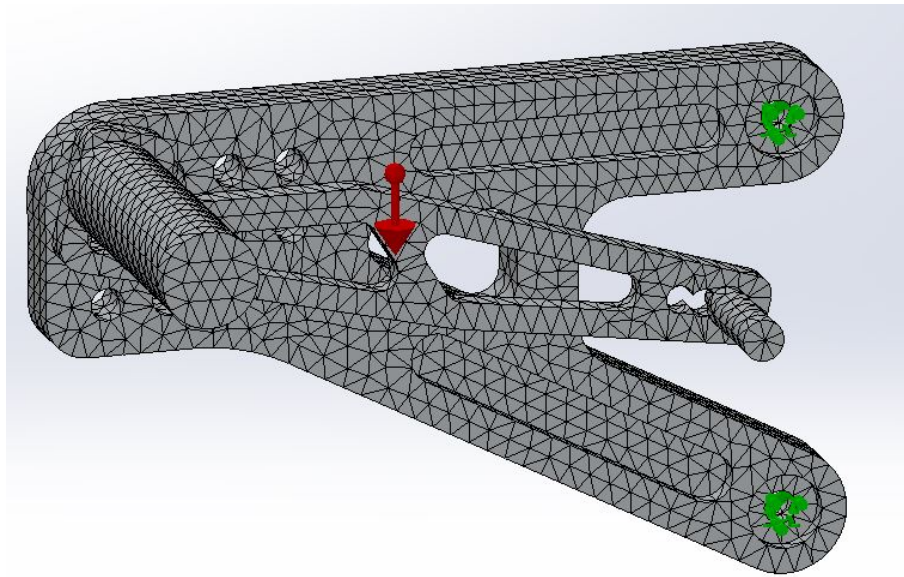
Mallado y cargas aplicadas (Diseño definitivo estribera derecha).
